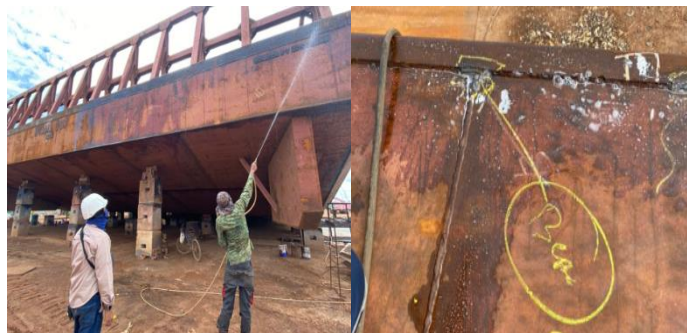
144. *Visual Weld Inspection Double Bottom Tank
